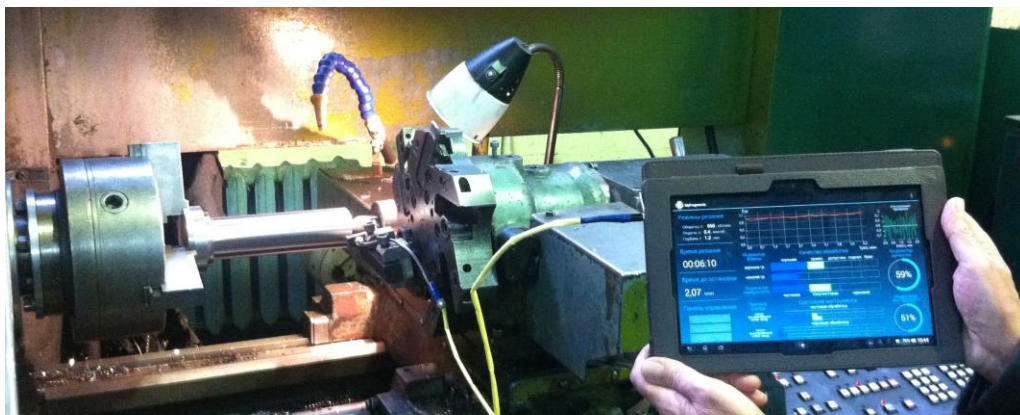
Автоматизированный контроль динамического поведения обрабатывающей системы токарного станка
